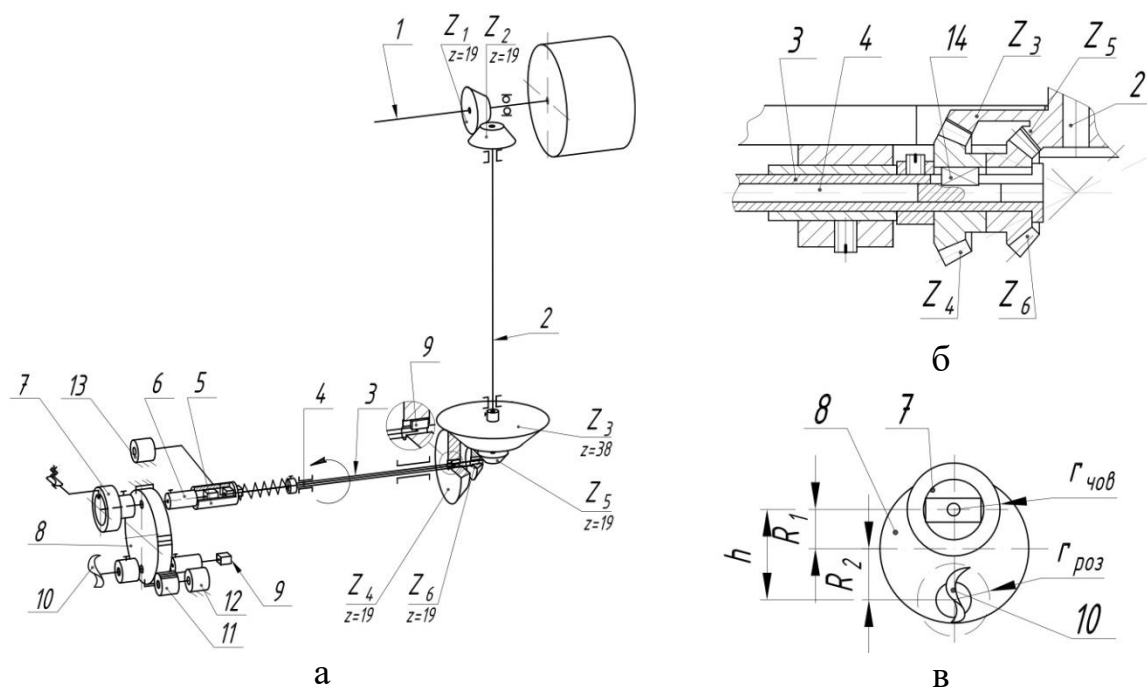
Розрахункова схема приводу петлетворних органів (човника та розширювача) а – кінематично-принципова схема механізму, б – конструктивна схема блока зубчастих коліс Z3-Z6, в – розрахункова схема положення валів човника та розширювача
